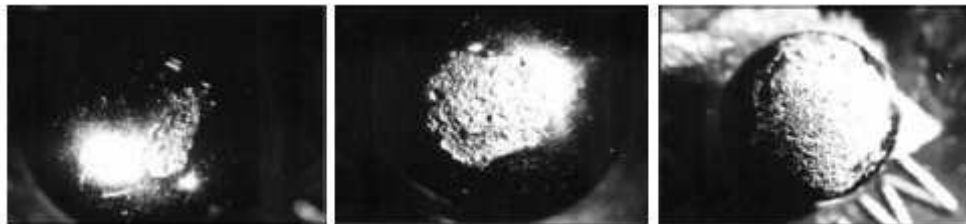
Rodamientos con defecto en bola. [T4]
